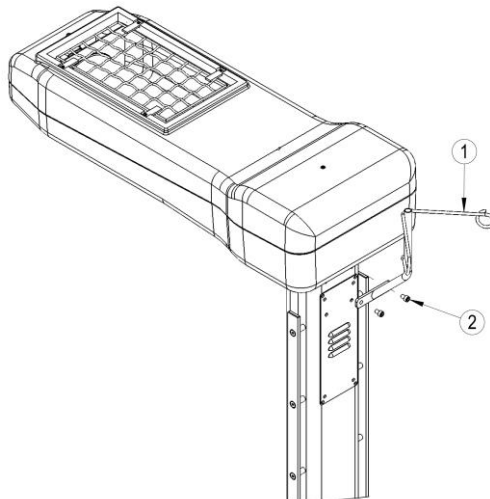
Montagem do Suporte de Soro Menor Fixo
